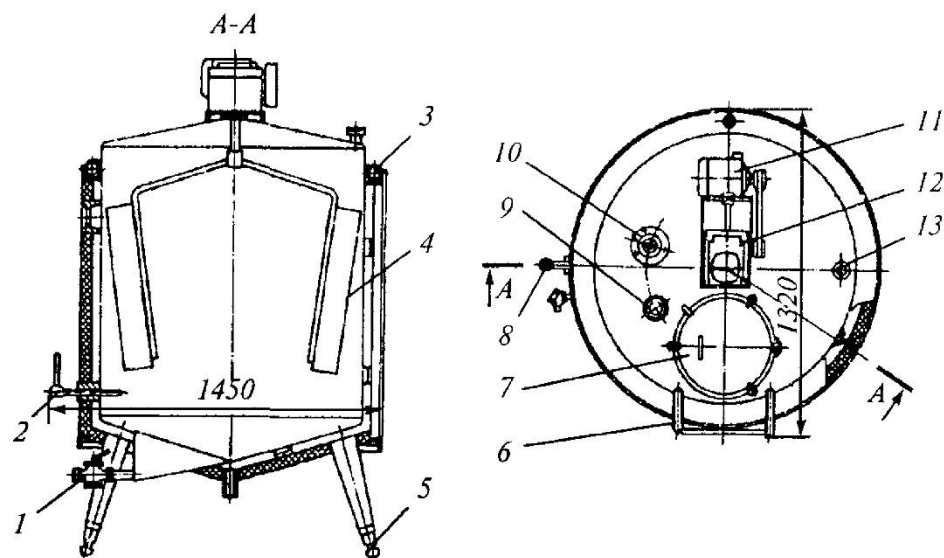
Резервуар вершкодозрівальний ОТН-1000
